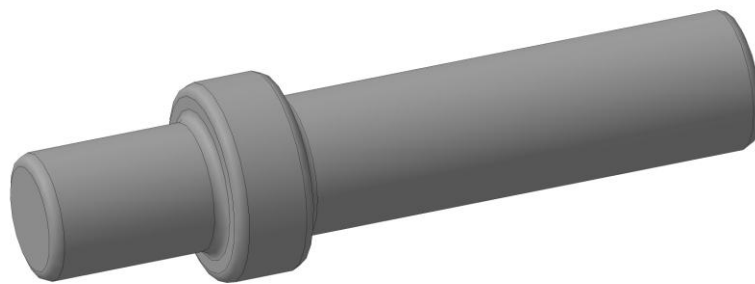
Заготовка деталі «Оправка» у КОМПАС 3D
